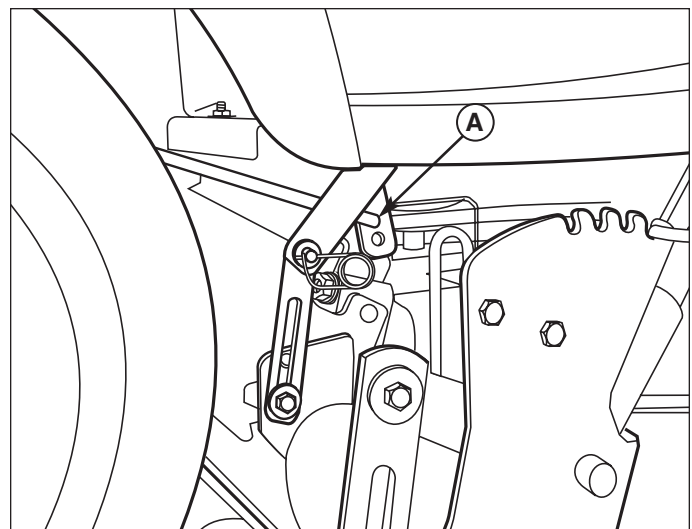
Réglage du levage de la tondeuse (vu de dessous le côté droit du tracteur)
